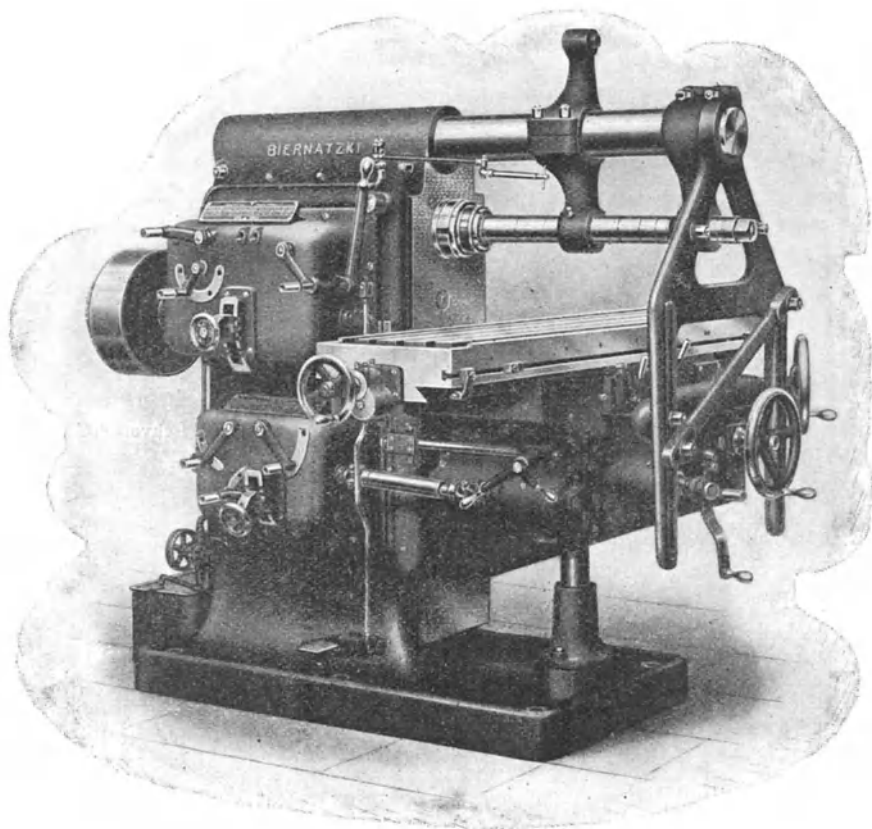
Die Hochkraftfräsmaschine von Biernatzki & Co.
